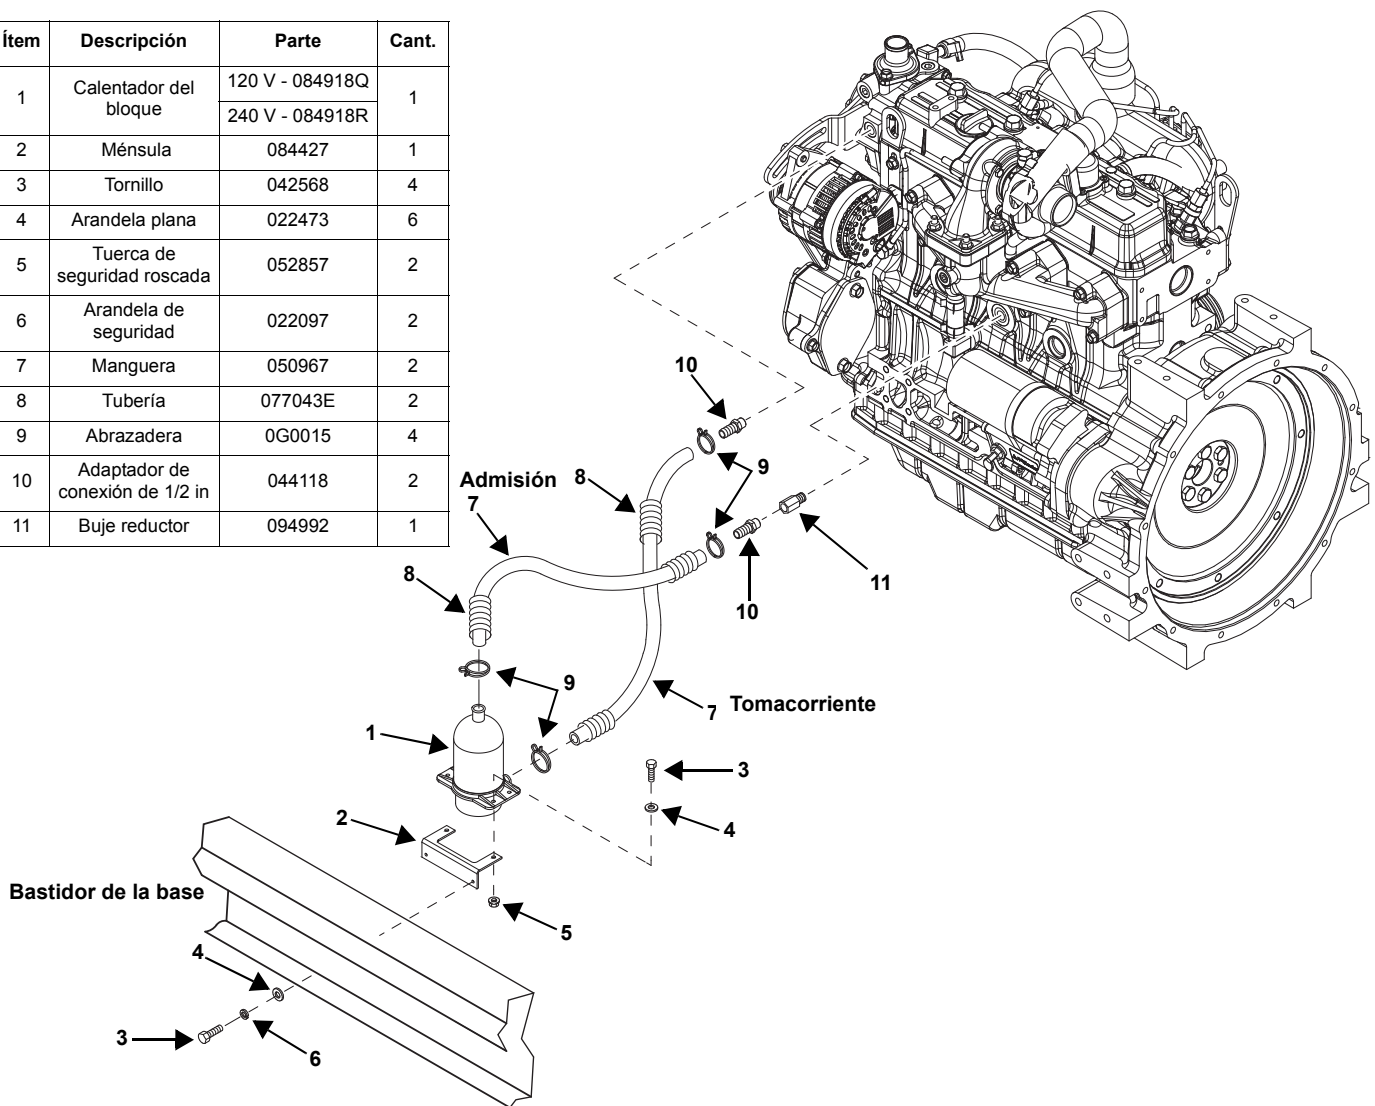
Conjunto de calentador de bloque (despiece, modelos de 2.4 l)
